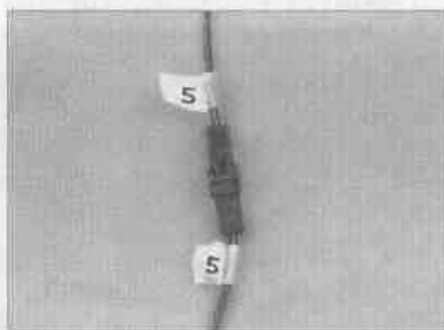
Перед рассоединением электрического разъема/шпунтового соединения отметьте оба конца соответствующего провода и шланга
